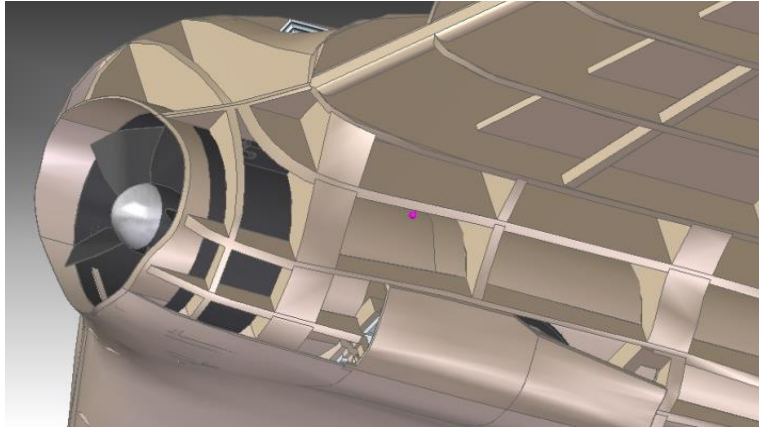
Vista de motor en estructura de fuselaje y cubierta frontal del ducto de aire.
